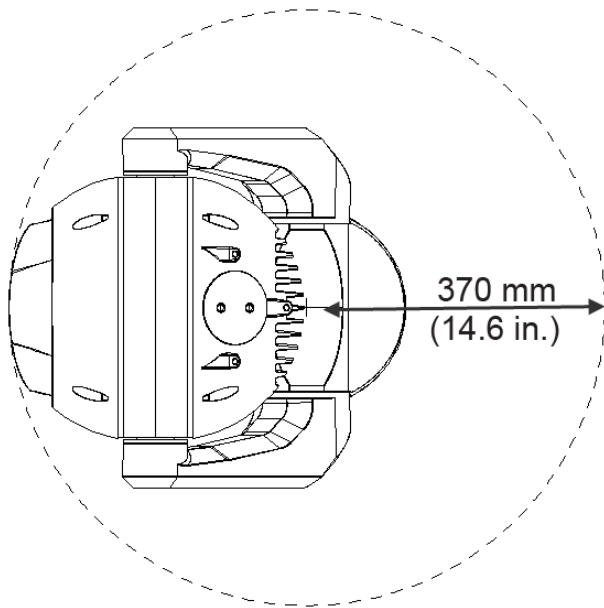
Зазор для обеспечения панорамирования камеры MIC7000, вид сверху
